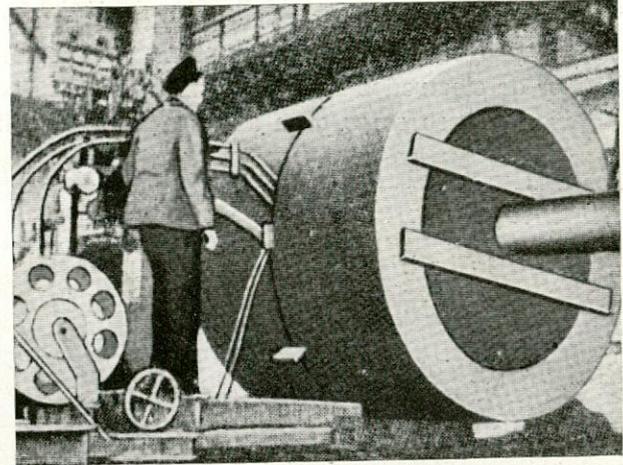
Soldadura de una costura circular de 18" de espesor por el procedimiento "Electro-slag", en un cilindro de una prensa hidráulica.
